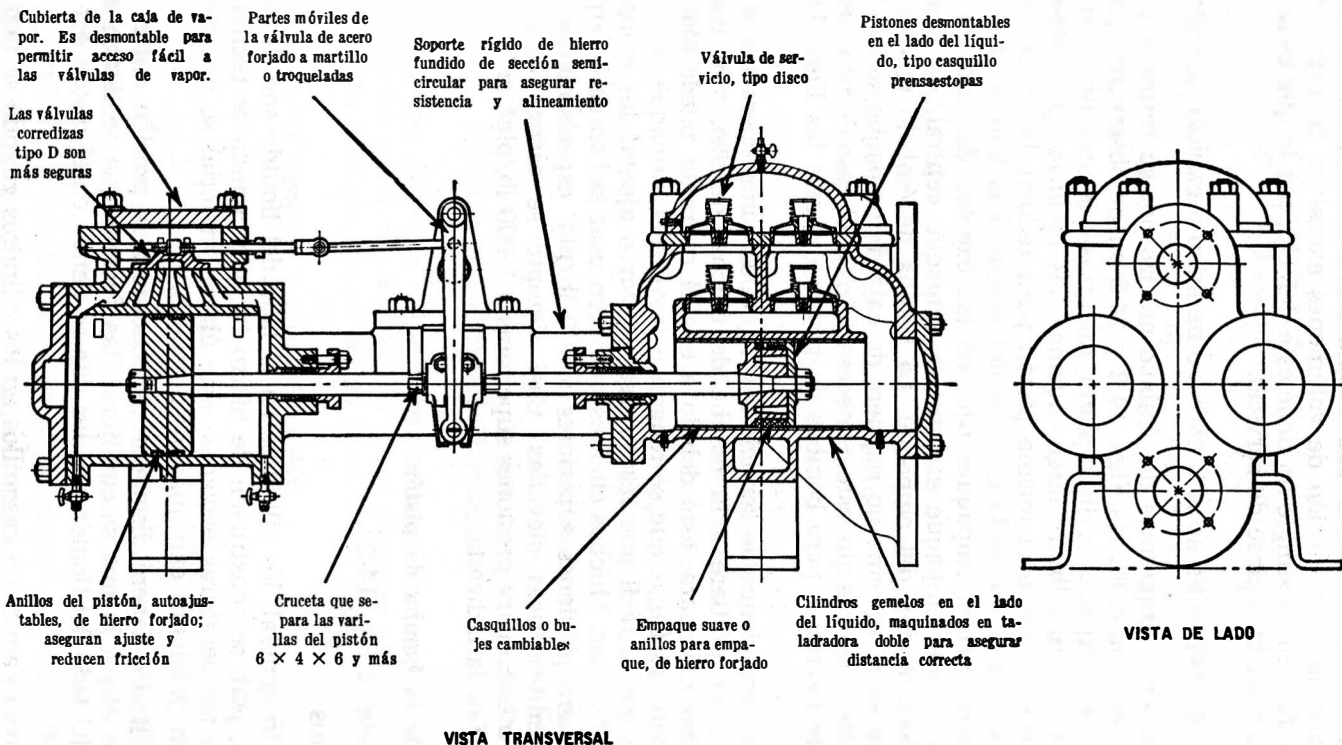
Bomba horizontal con pistones gemelos. (Cortesía de Worthington Corporation.)
